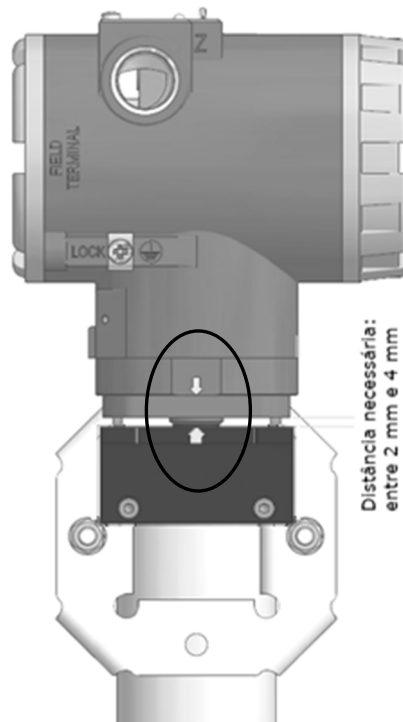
Montagem do VTP10-P em ímã linear.
